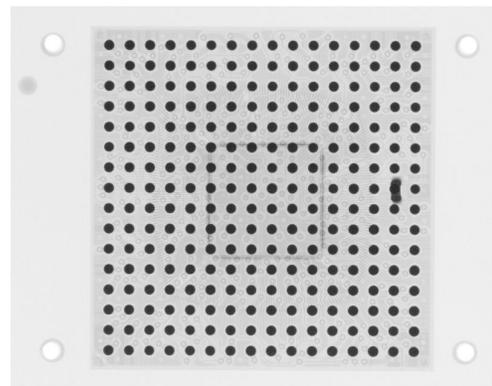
Radiografía del chip BGA de 256 bolitas, soldado en la placa de pruebas.
